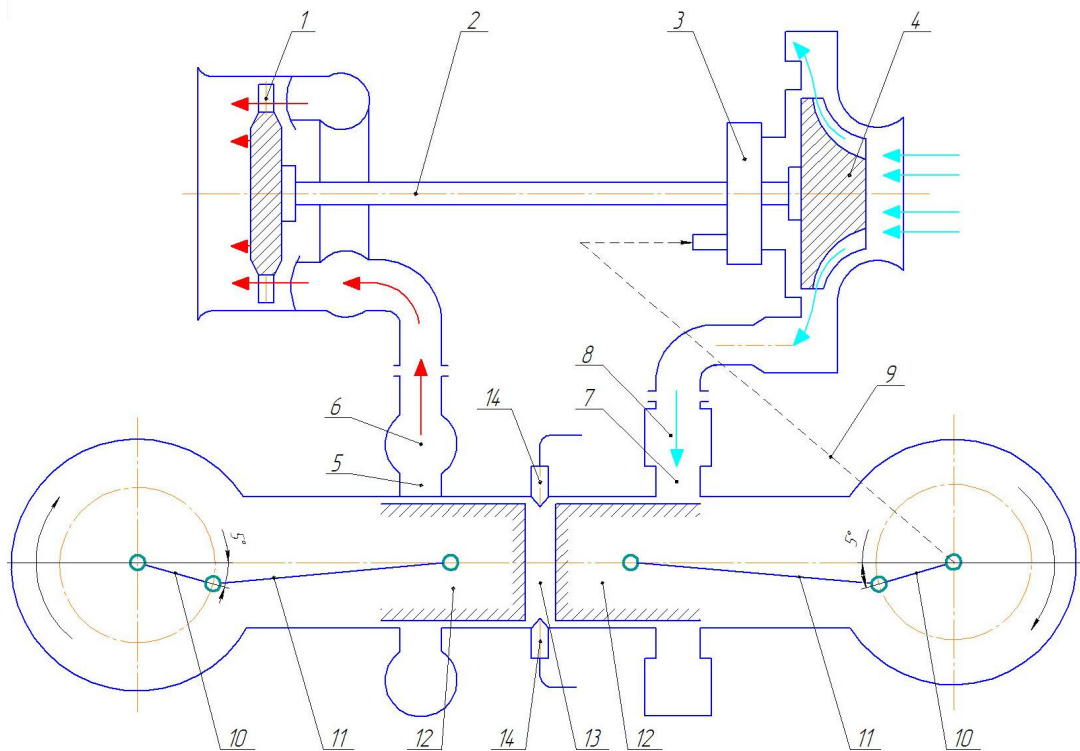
Схема двигуна 6ТДФ (6ДН 12/2х12): 1 – газова турбіна; 2 – ресора; 3 – редуктор; 4 – компресор; 5 – випускні вікна; 6 – випускні колектори; 7 – впускні вікна; 8 – впускний ресивер; 9 – механізм передач; 10 – колінчаті вали; 11 – шатуни; 12 – поршні; 13 – камера згоряння; 14 – форсунки
